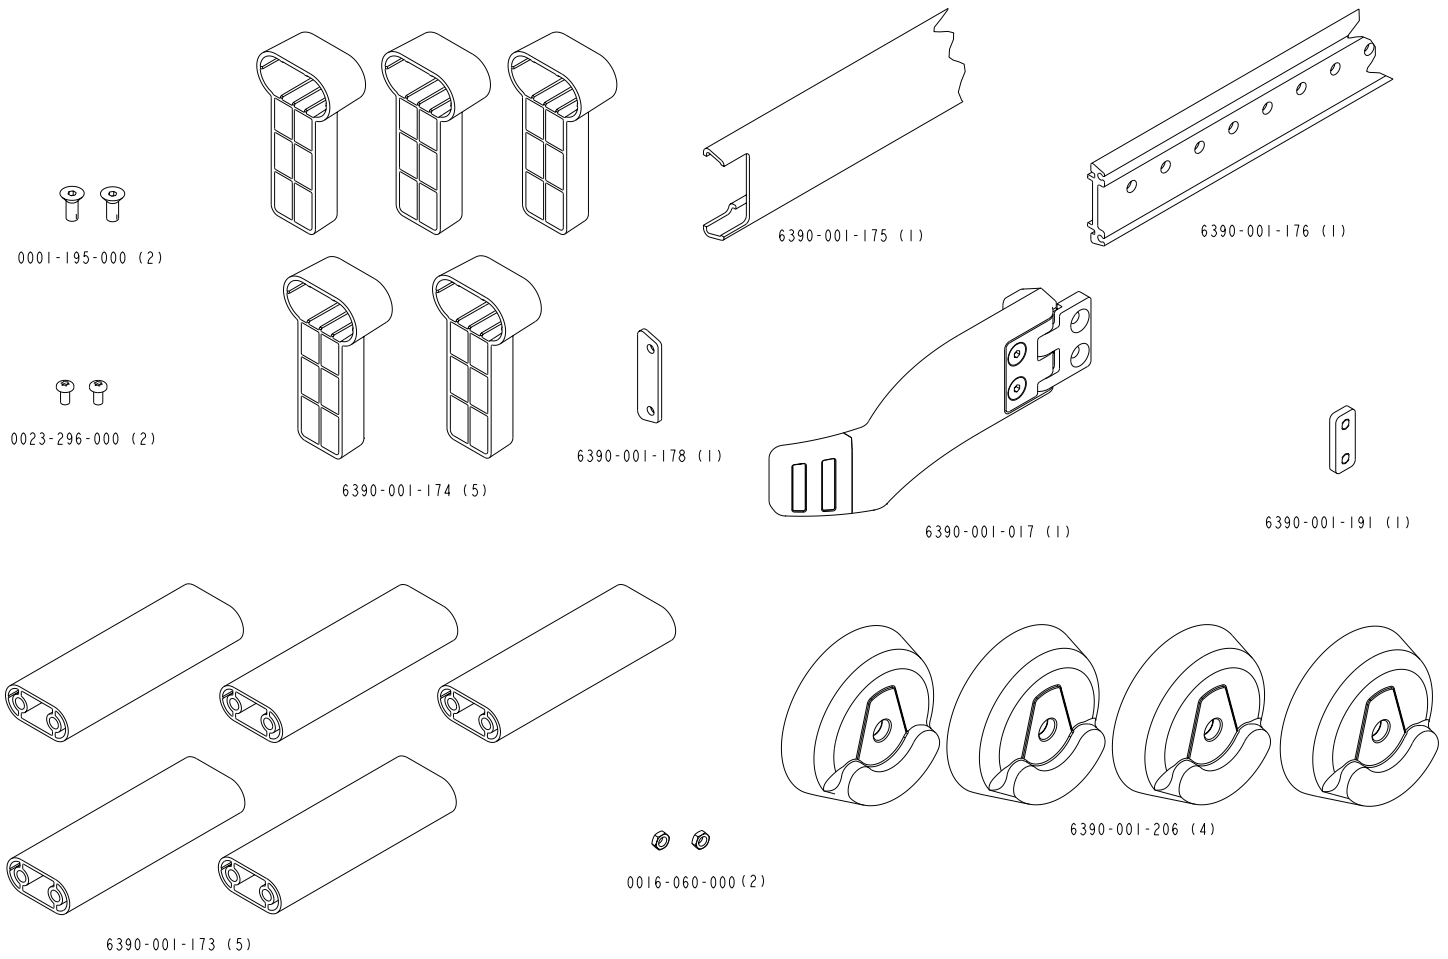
Composants du kit d'installation de l'ensemble de guidage des roues en option 6390-027-000
